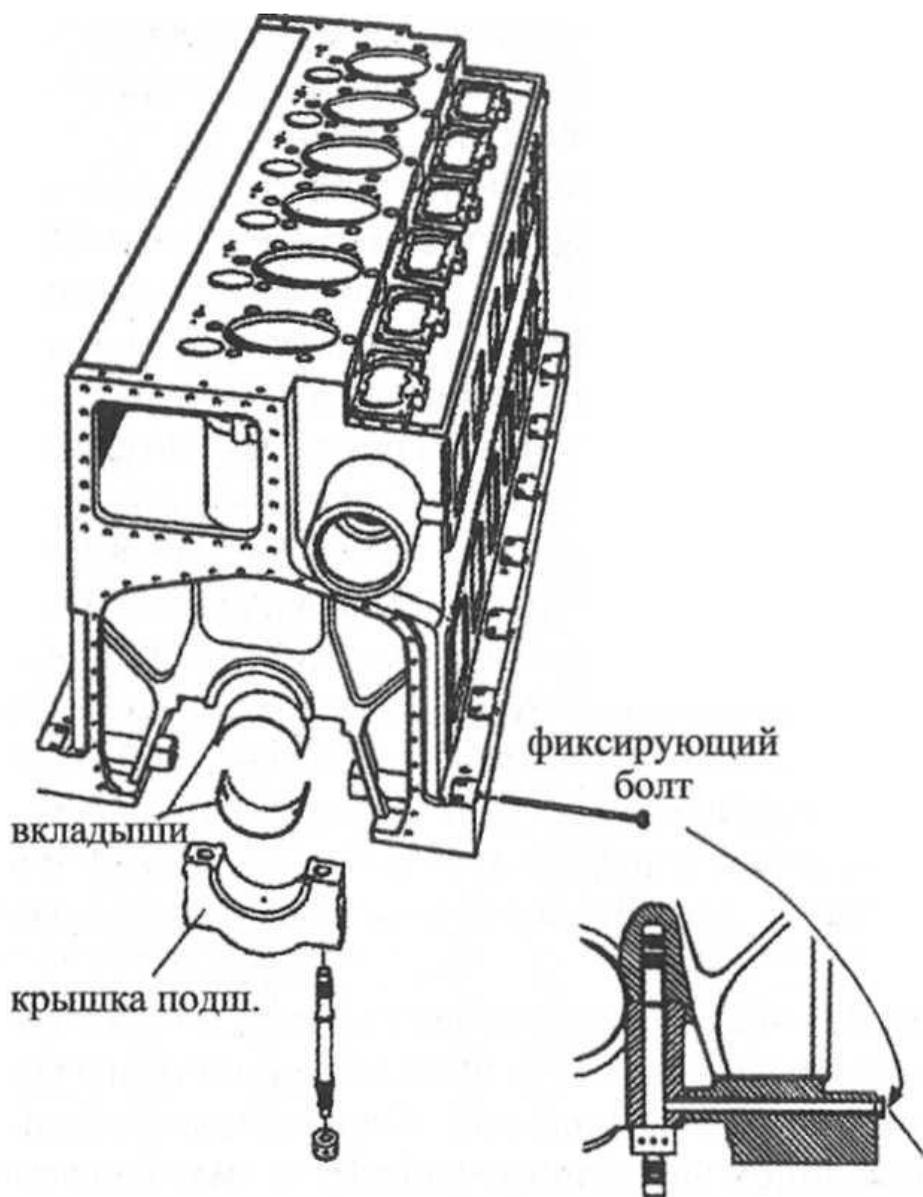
Станина-блок цилиндров, крепление рамовых подшипников
